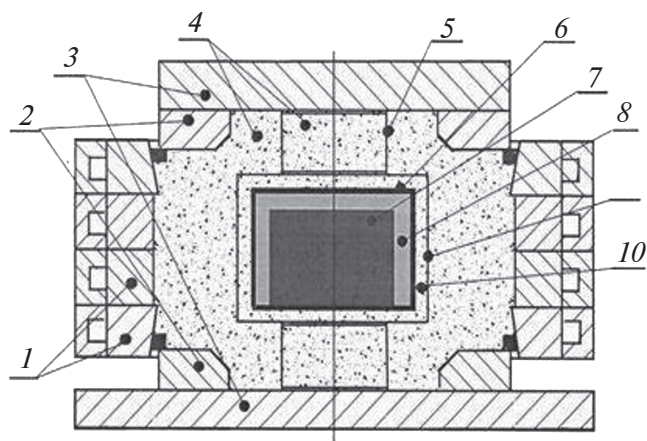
Схема аппарата высокого давления: 1 – силовые кольца цилиндра; 2 – поршни; 3 – опорные плиты; 4 – песок; 5 – токоподвод; 6 – контейнер; 7 – графит; 8 – матричный металл; 9 – нагреватель; 10 – электроизоляция.
